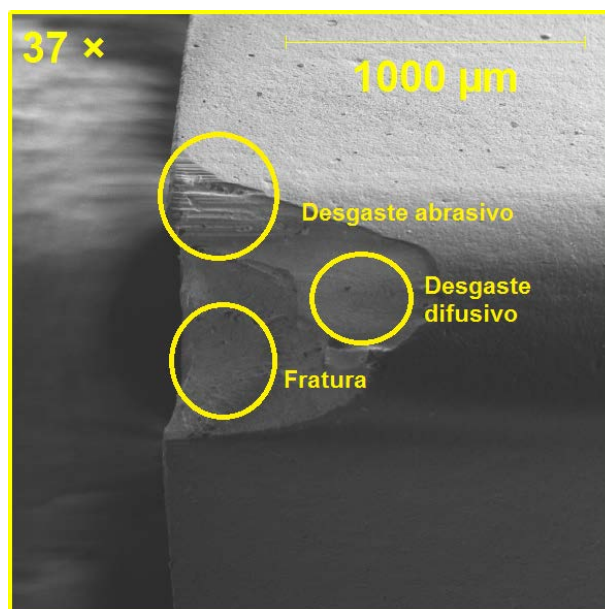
Imagem MEV da superfície de folga da ferramenta com recobrimento AlCrN nanoestruturado após a usinagem com velocidade de corte de 200 m/min, e avanço de 0,10 mm/rev, profundidade de usinagem de 0,25 mm.
